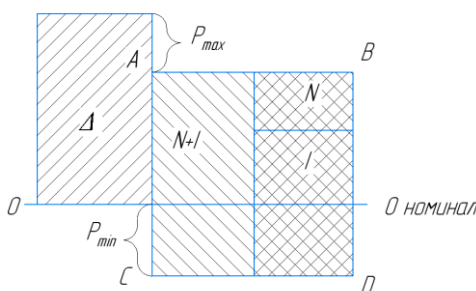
Поле допуска на диаметр развертки
